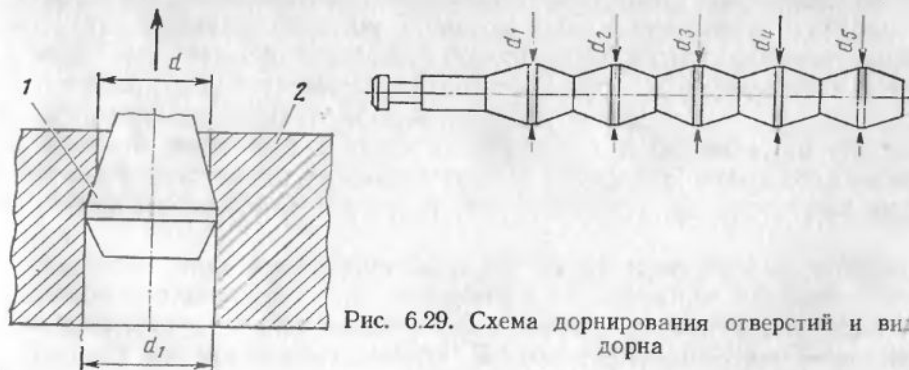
Схема дорнирования отверстий и вид дорна
